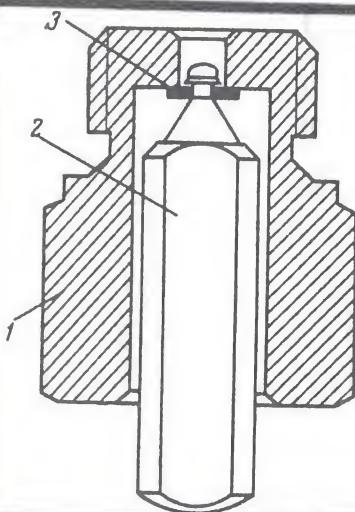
Конструкция топливного клапана карбюратора К-126: 1 — корпус; 2 — игла; 3 — уплотнительное кольцо — шайба из СКУ-6.
